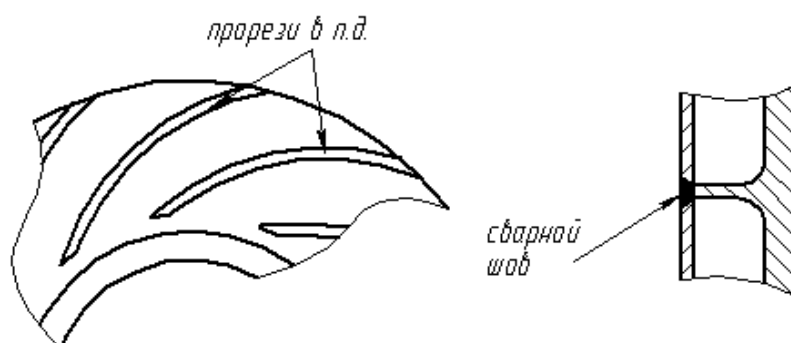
Схема сварки покрывающего диска и лопаток через прорезы в покрывающем диске
